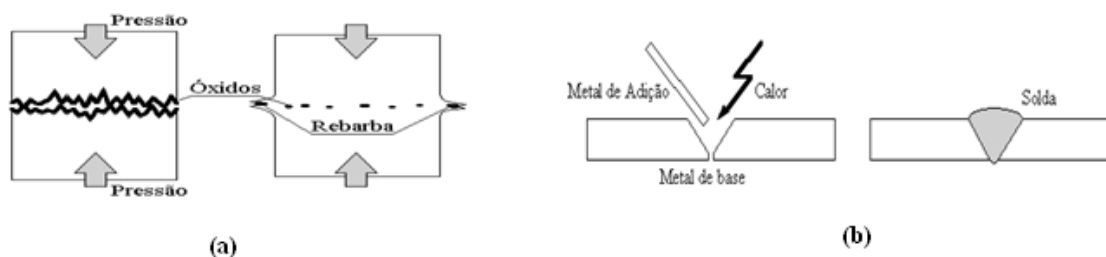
(a) Soldagem por pressão. (b) Soldagem por fusão (MODENESI et al., 2005).
